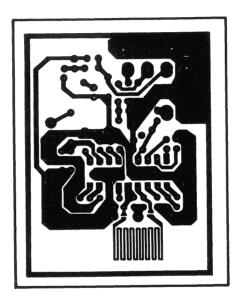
Circuit imprimé (côté soudure)
